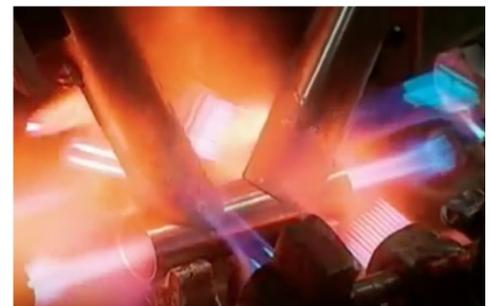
Imagen proceso de soldadura del aluminio
